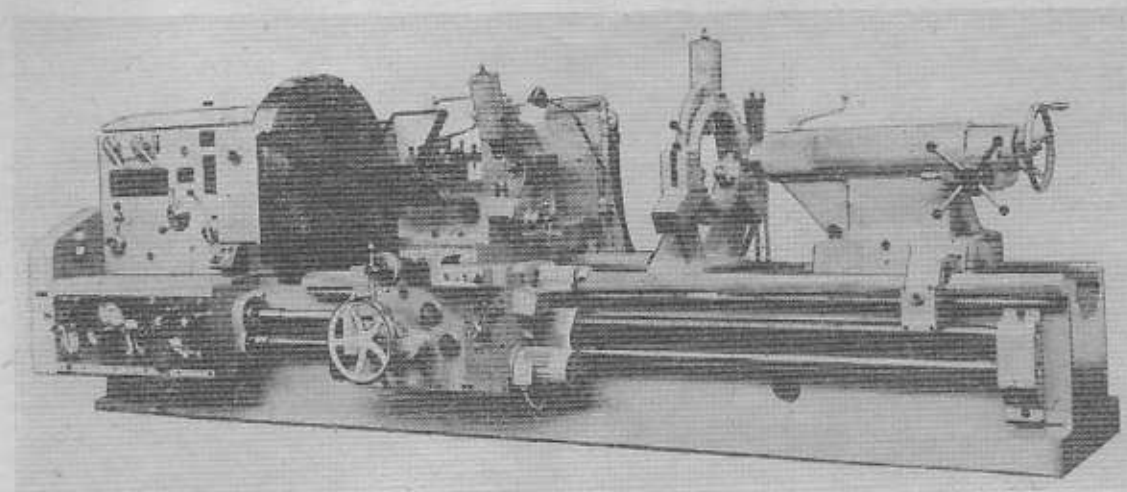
Общий вид токарно-винторезного станка модели 1M65
